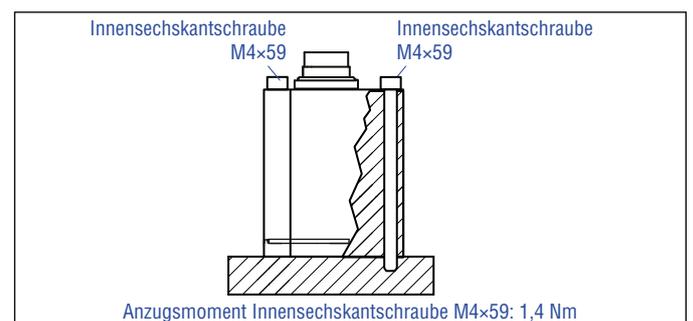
Befestigung mittels Innensechskant-Schrauben M4×59
